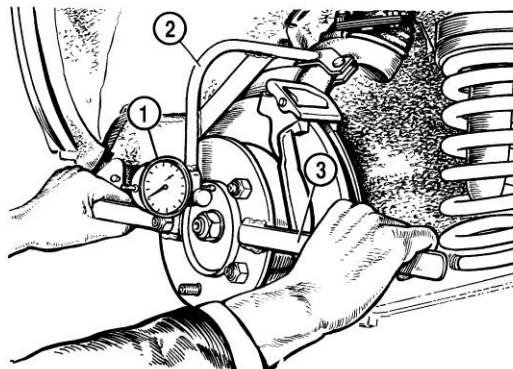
Перевірка осьового зазору в підшипниках маточини переднього колеса
